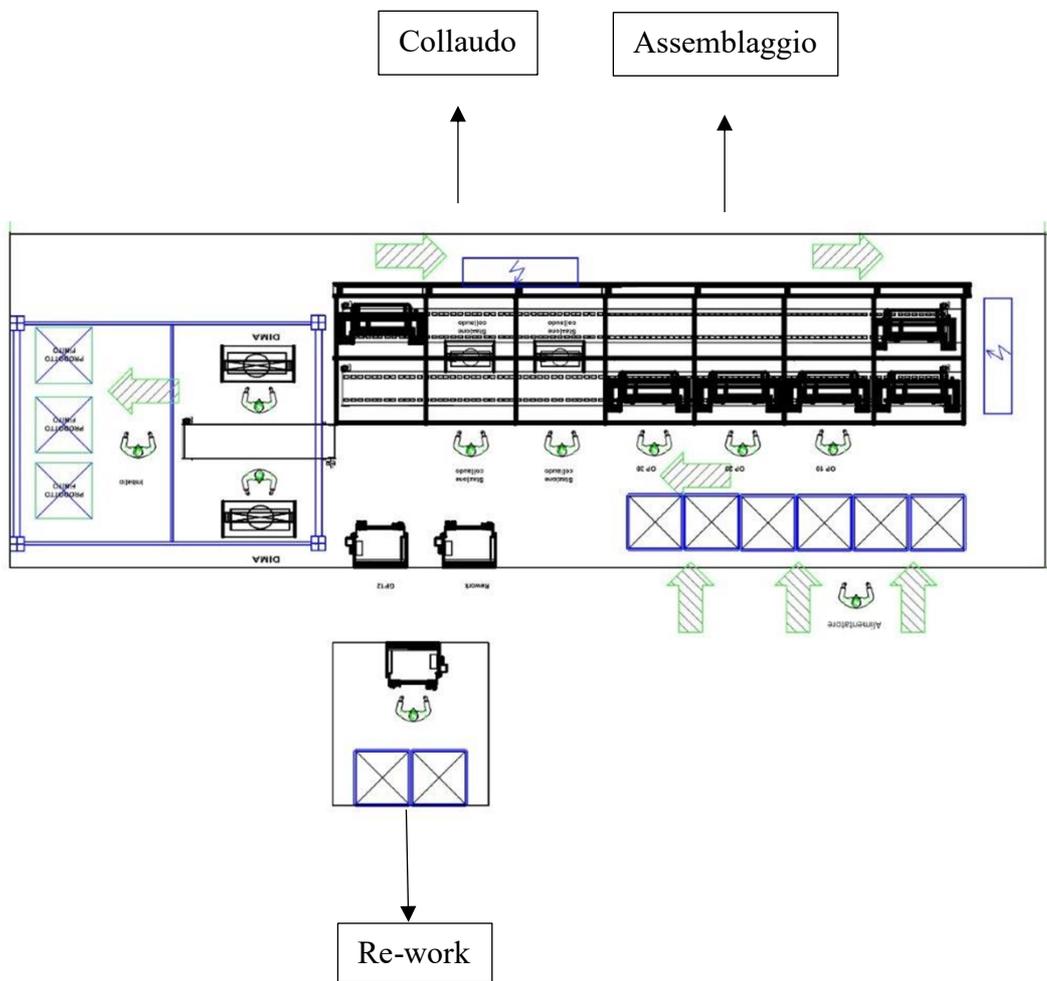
Banco di assemblaggio, collaudo e re-work
